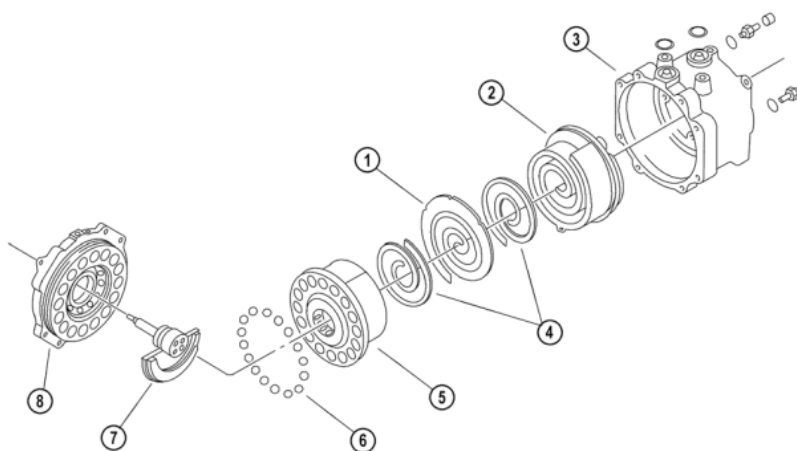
Спиральный компрессор: 1 – упорная пластина;
